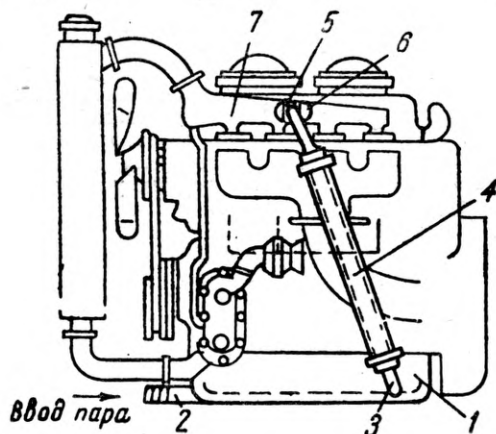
Схема устройства подогрева двигателя ЯАЗ-204А паром от ППУ-3
